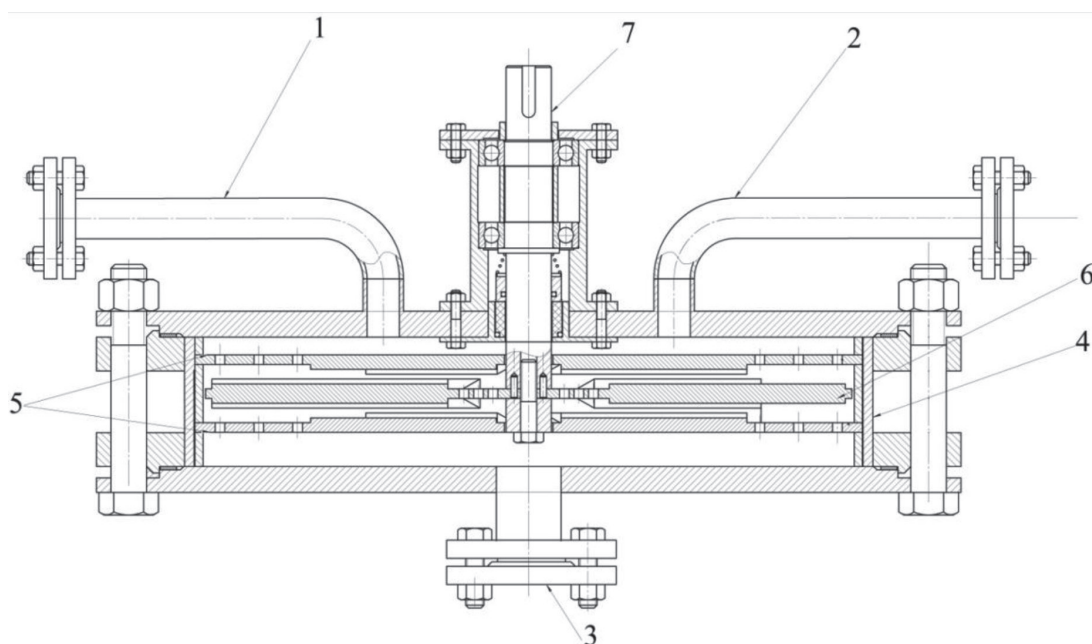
Роторно-дисковый смеситель: 1, 2 – патрубки для ввода продуктов эмульгирования; 3 – выходной патрубков, 4 – корпус; 5 – неподвижные диски; 6 – подвижный диск; 7 – вал ротора
